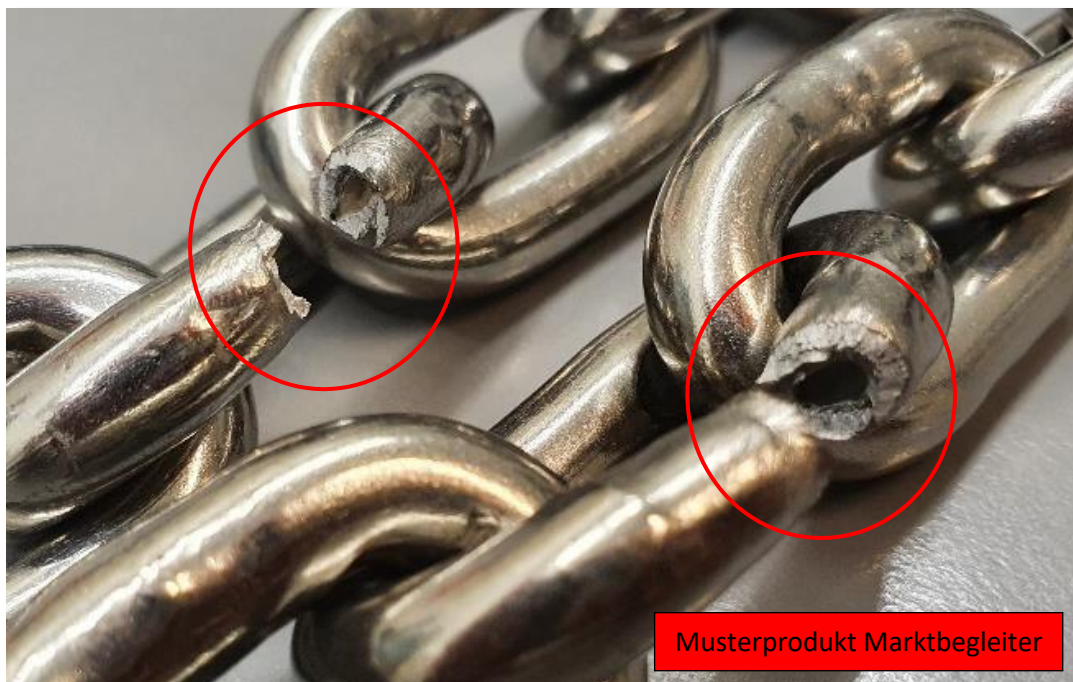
8x24 mm Schweißnahtbrüche beim Zugversuch
